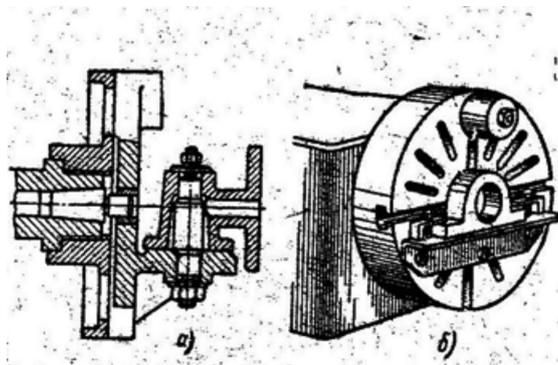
Патрон специальной конструкции с креплением обрабатываемой детали на угольнике:
